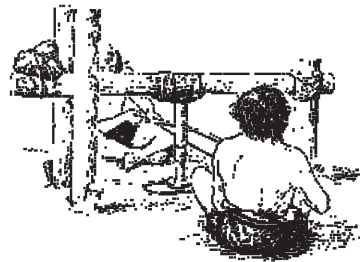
Свердлувальний верстат з подвійним приводом
